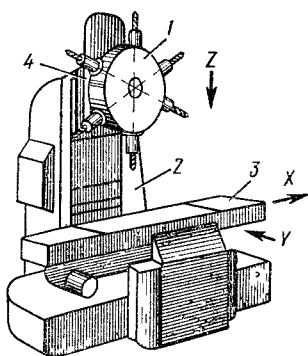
Компонка вертикально-фрезерного станка с револьверной головкой
